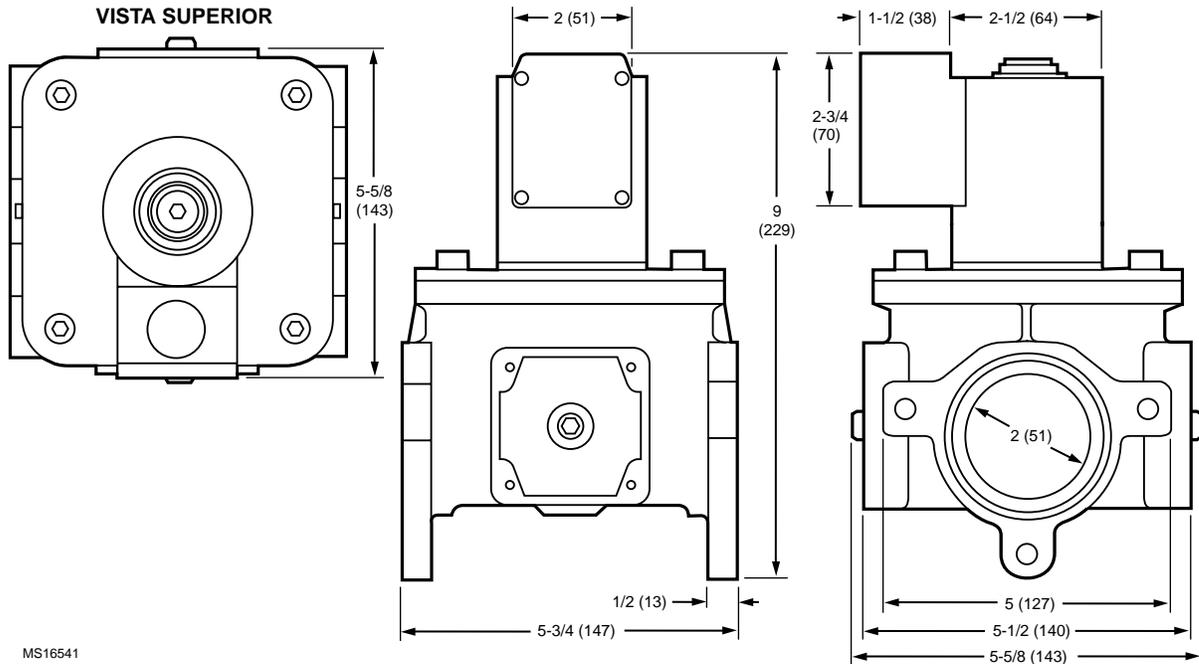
Dimensiones Aproximadas de la V4297A1005 en pulg. (mm).
